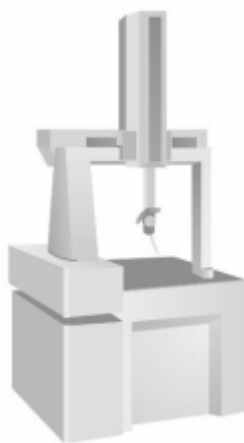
Jednosouřadnicový měřicí přístroj [10]
